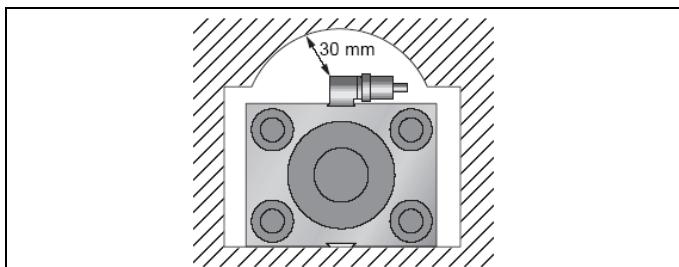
Distanza minima dei sensori rispetto alle protezioni ecc.
